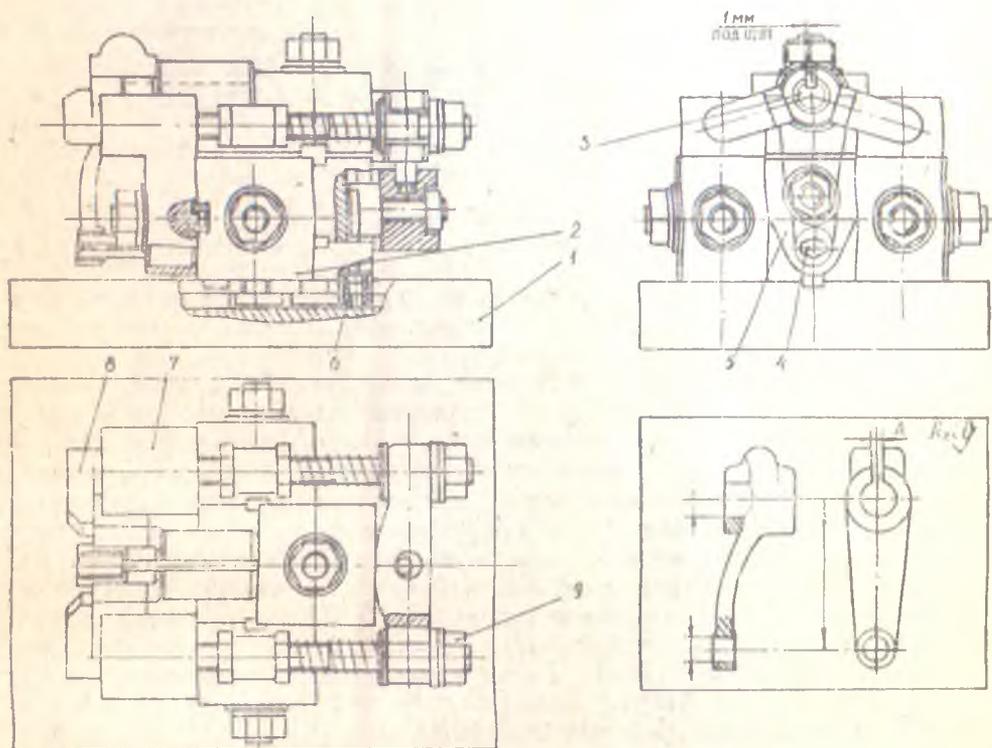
Универсально-сборное приспособление для фрезеровки паза в заготовке
